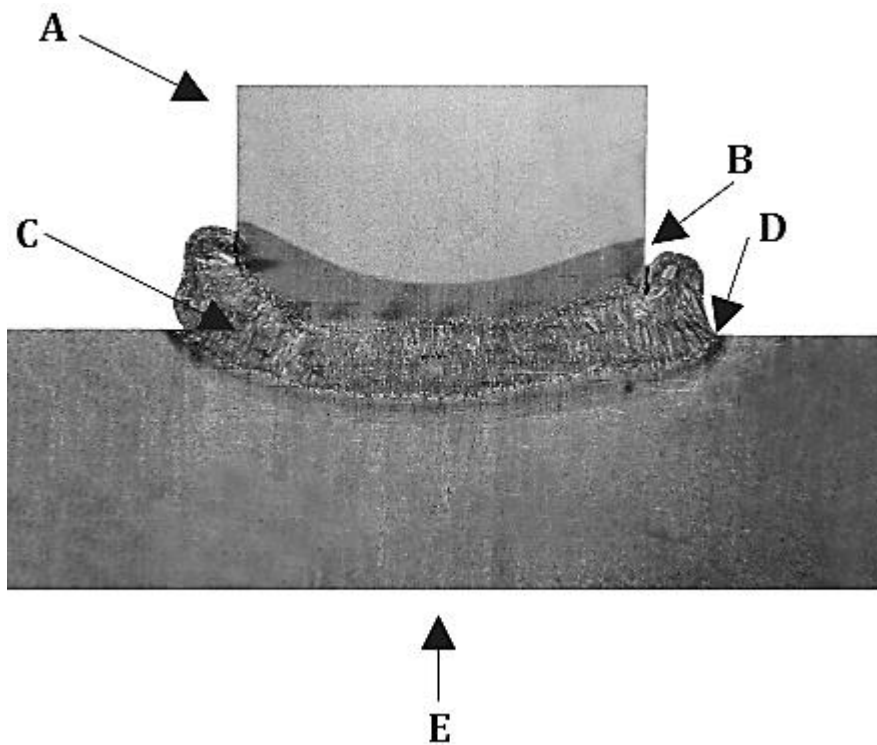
Macrografia da seção longitudinal de um pino soldado.
